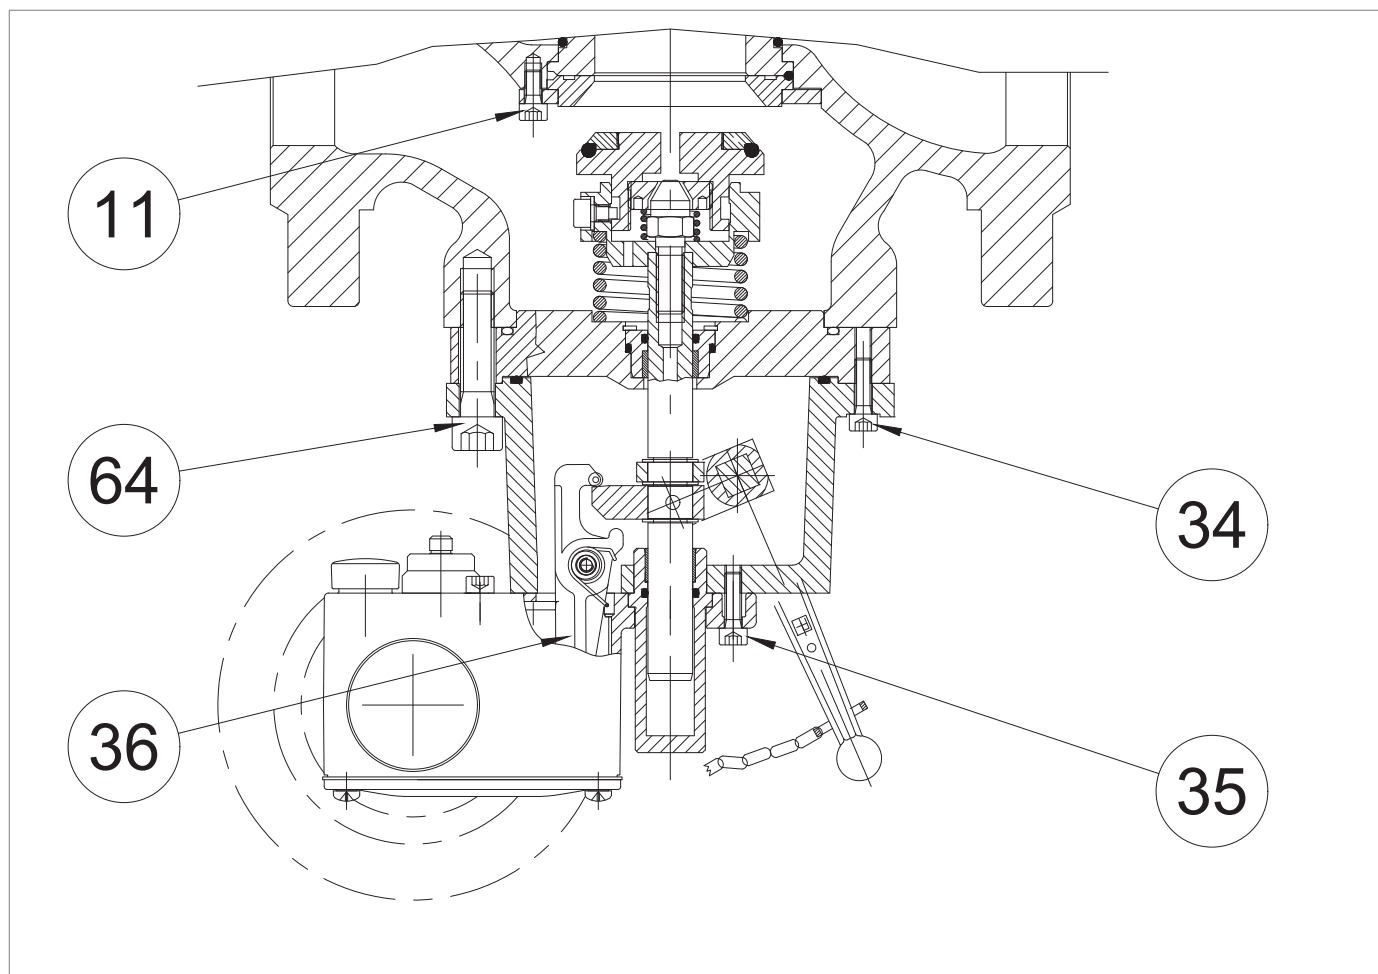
Моменты затяжки предохранительного запорного клапана SB/82 2"
